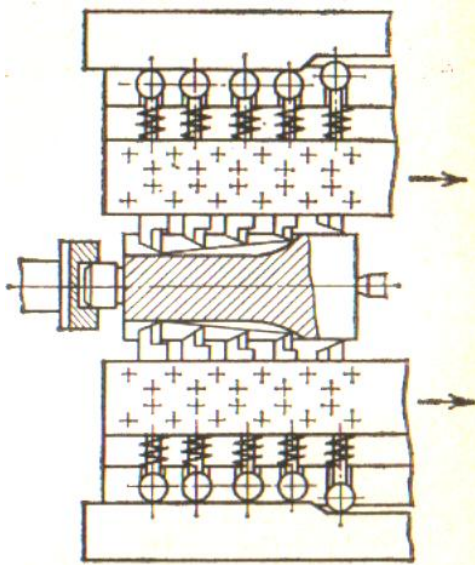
Схема формирования наружных шлицев двумя блочными протяжками
